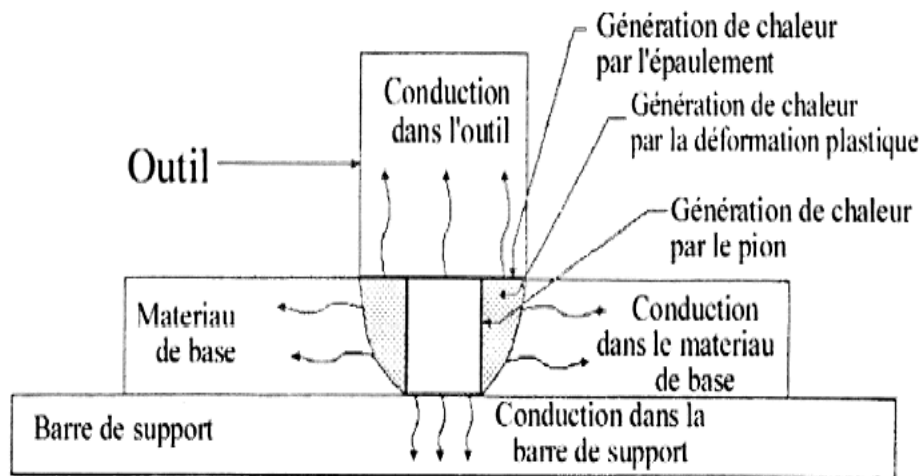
Transferts de chaleur au cours du soudage par friction malaxage [2].
